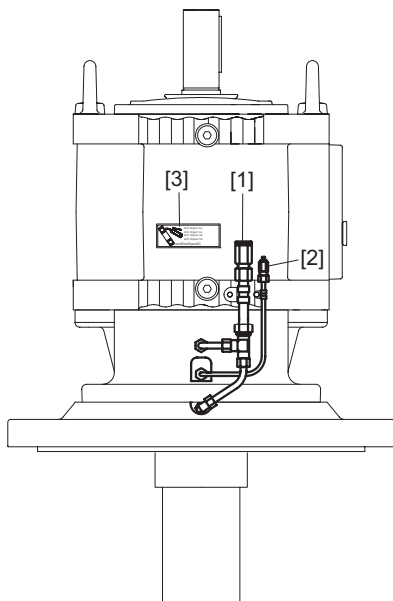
Смазка редукторов с системой Drywell (на рисунке редуктор EBD-версии) 57378AXX
